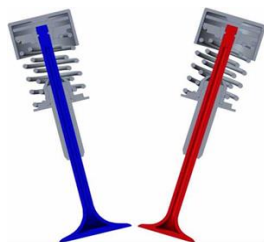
Schéma rozvodového mechanismu DOHC pro projektovaný motor [13]
